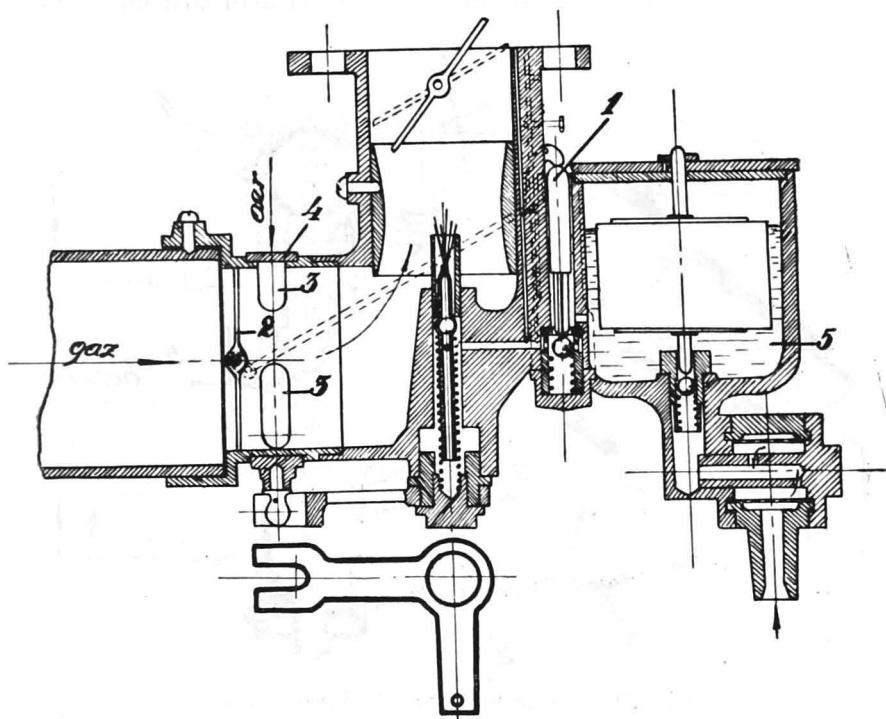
Amestecătorul-carburatorul *Barbier*.
